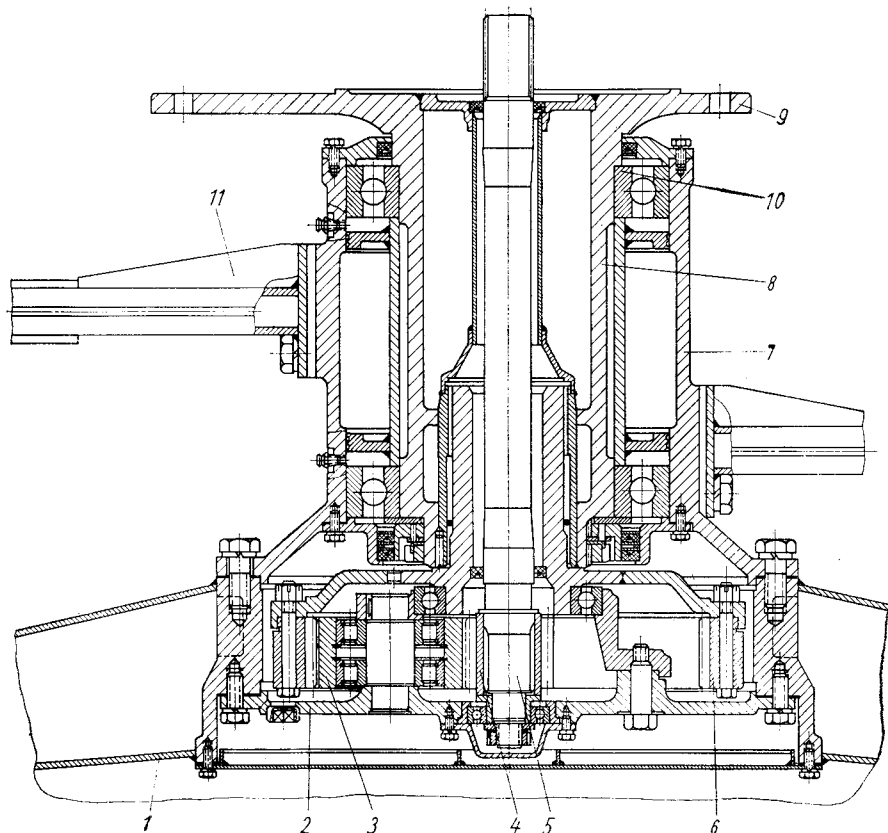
Планетарный редуктор экскаватора-каналокопателя Д-583:
